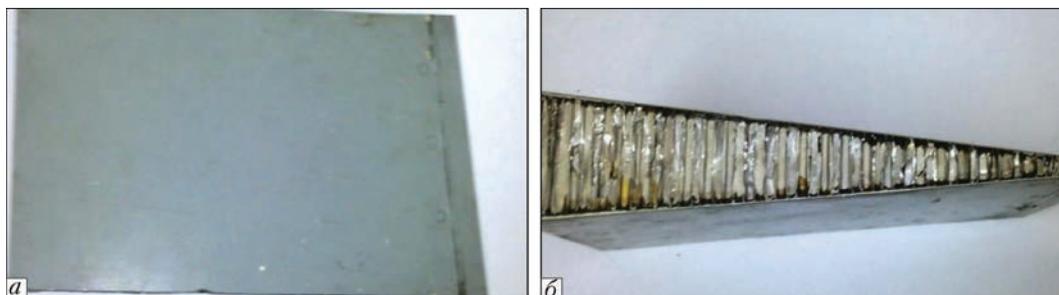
Сотовая конструкция закрылка крыла самолета: а – вид сверху; б – вид сбоку
